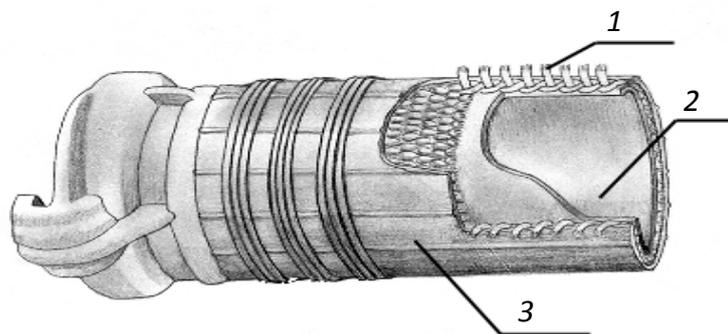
Конструкция напорного рукава с внутренним гидроизоляционным покрытием и защитным покрытием каркаса:
